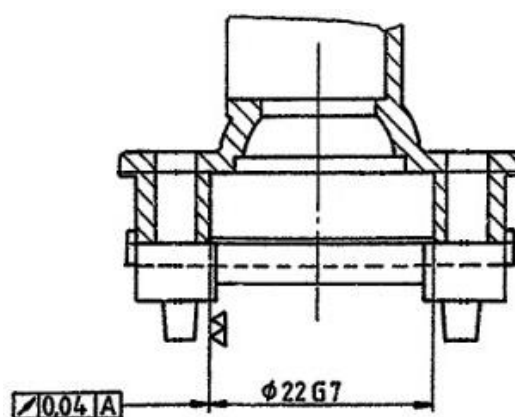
Toleranciamento do furo de diâmetro 22 mm
